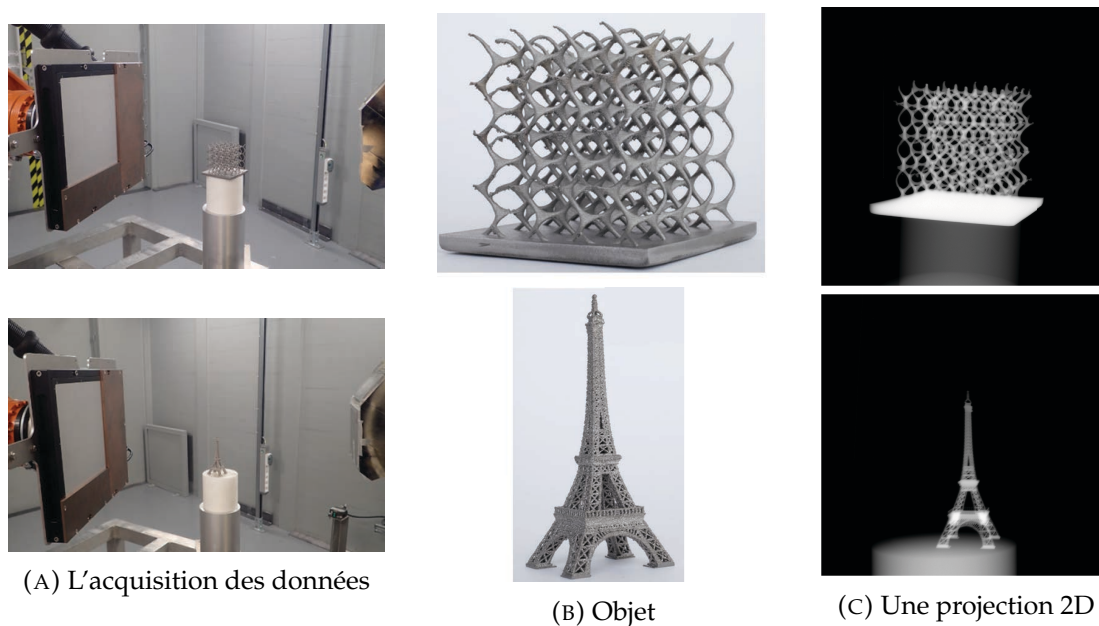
Inspection de deux composants créés par fabrication additive.
